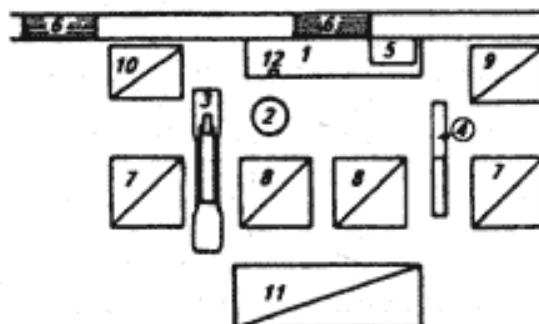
Схема расположения приспособлений, инструментов и материалов на рабочем месте бондара:
